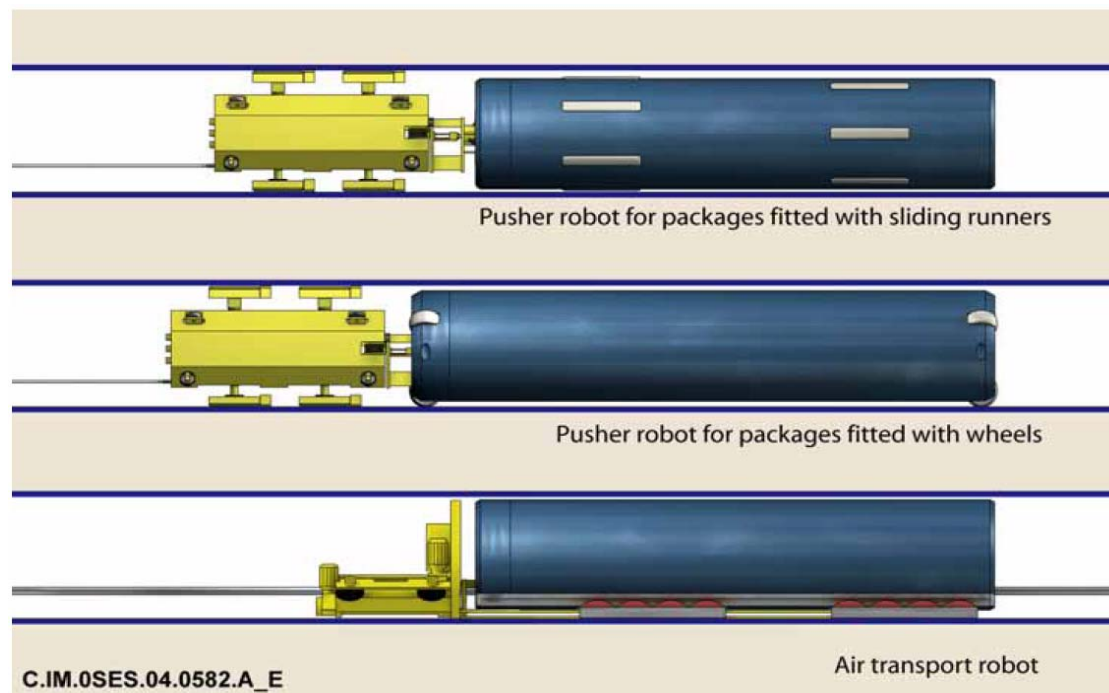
Untersuchte Möglichkeiten für das Einschleiben eines Endlagerbehälters für ausgediente Brennelemente in den Einlagerungstunnel – Frankreich /2-24/
